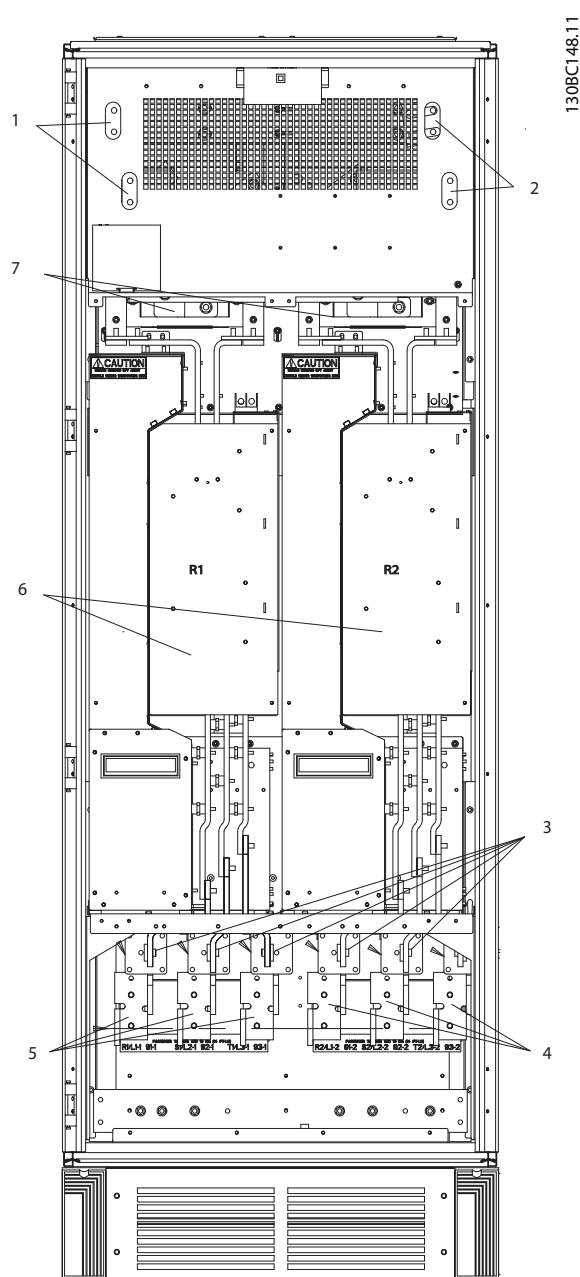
Шкаф выпрямителя, размеры корпуса F10 и F12
